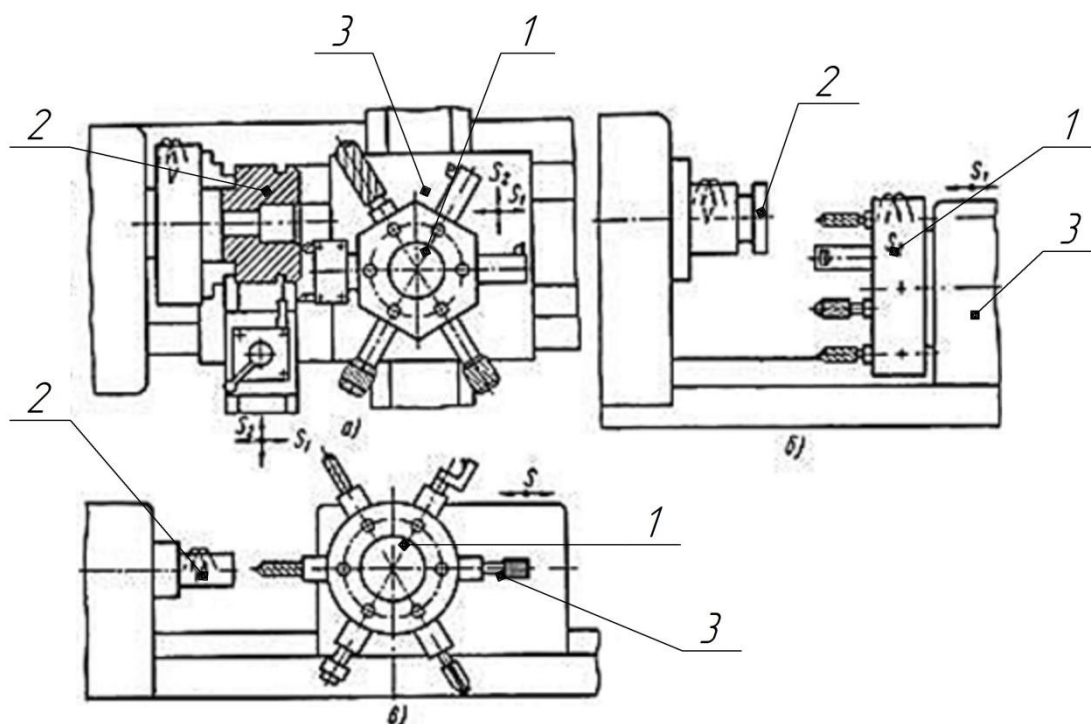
Розміщення револьверних головок: а) з вертикальною віссю обертання; 1 – револьверна головка; 2 – оброблювана деталь; 3 – револьверний супорт; б) з горизонтальною віссю обертання паралельної осі шпинделя: 1—револьверна головка; 2—оброблювана деталь; 3—револьверний супорт; в) з горизонтальною віссю обертання перпендикулярній осі шпинделя: 1—револьверна головка; 2—оброблювана деталь; 3—револьверний супорт;
